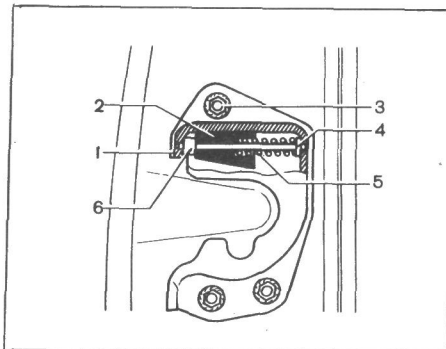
Фиксатор замка двери: 1 — корпус фиксатора; 2 — сухарь; 3 — болт; 4 — ось; 5 — пружина; 6 — втулка
